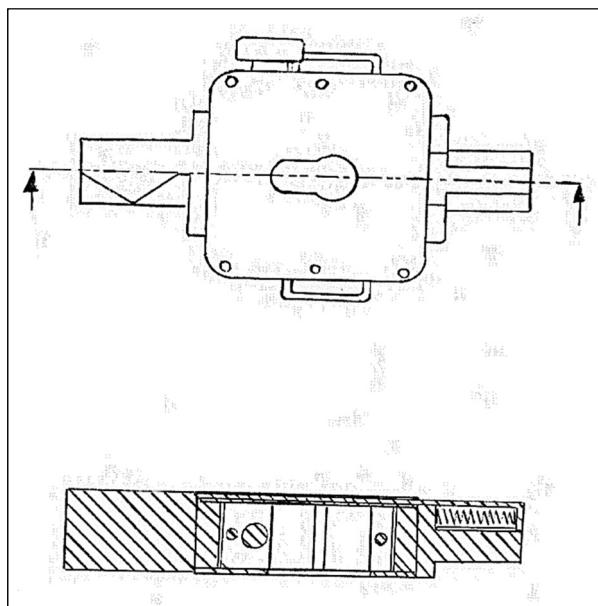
Vue de dessus et vue de coupe de l'adaptateur universelle
